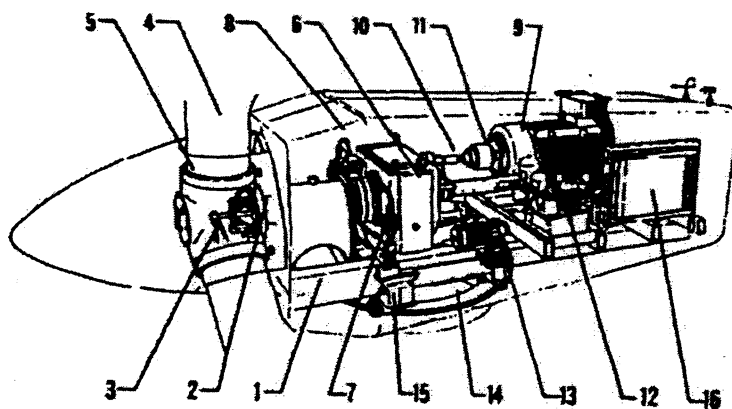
Привод ветряной электростанции *Vestas V20*: 1 - рама; 2 - главный вал; 3 - втулка; 4 - лопасти ветряка; 5 - подшипник лопасти; 6 - редуктор; 7 - траверса; 8 - гидравлический тормоз; 9 - генератор; 10 - карданный механизм; 11 - муфта; 12 - гидроузел; 13 - электрические сервомоторы; 14 - торцовое зубчатое колесо; 15 - счетчик числа оборотов гондолы; 16 - центральный узел управления
